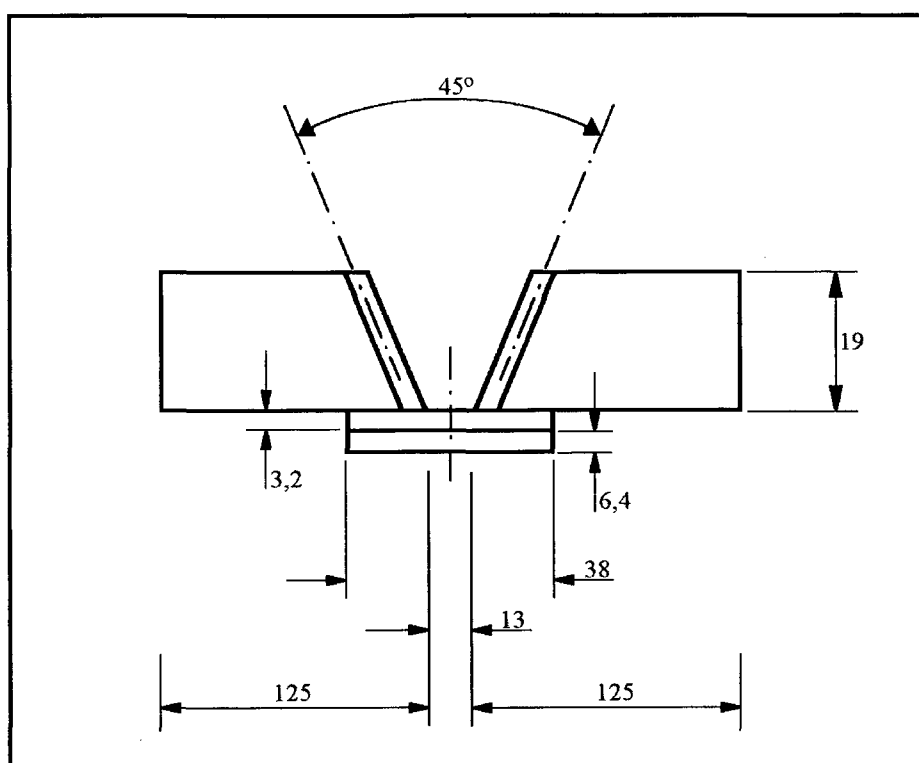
Esquema da seção transversal do chanfro. Soldagem semi-automática. Dimensões em mm.
